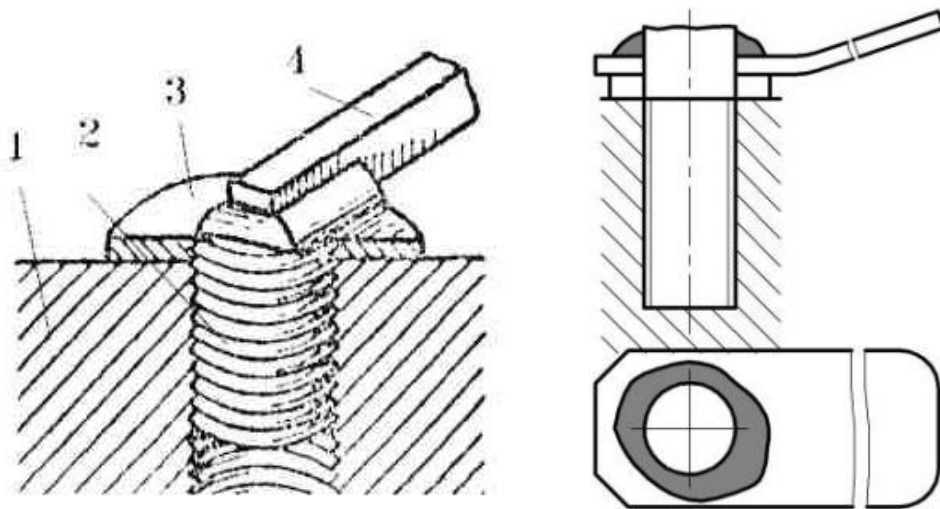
Приварена пластина з важелем: 1- корпус; 2- шпилька; 3- пластина; 4 – важіль
